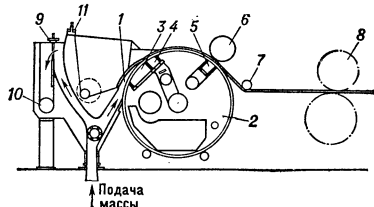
Схема бумагоделательной машины типа ротоформер: 1 — напорный ящик; 2 — вакуум-формирующий цилиндр; 3, 4, 5 — отсасывающие камеры; 6 — прижимной валик; 7 — бумаговедущий валик; 8 — пресс; 9 — устройство для регулирования уровня массы; 10 — труба для отвода перелива массы; 11 — регулирующее устройство.
